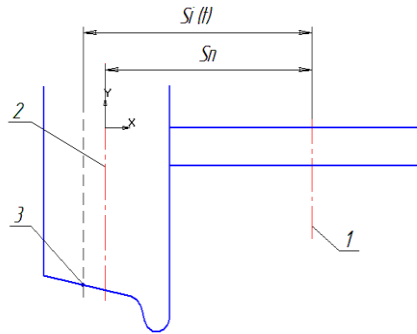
Розрахункова схема визначення відстаней від середини колісних пар до точки контакту колеса і рейки: 1 – середина колісної пари; 2 – середній круг катання колеса; 3 – точка контакту колеса і рейки
